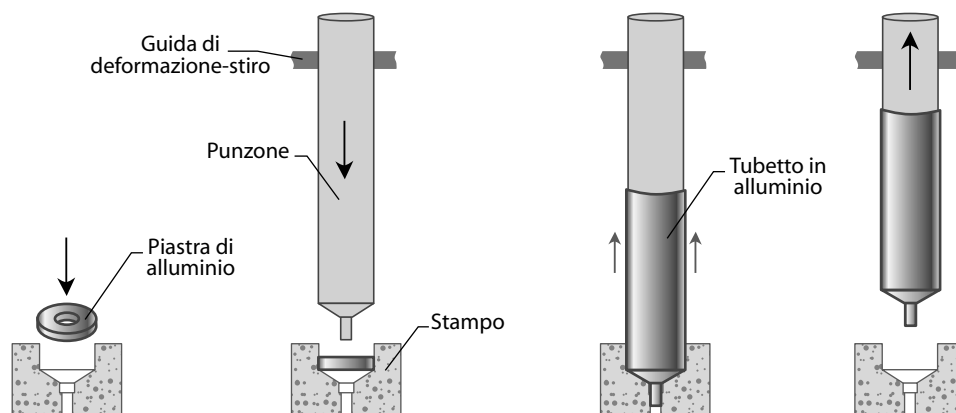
Estrusione e rimontaggio di tubetti deformabili in alluminio.
